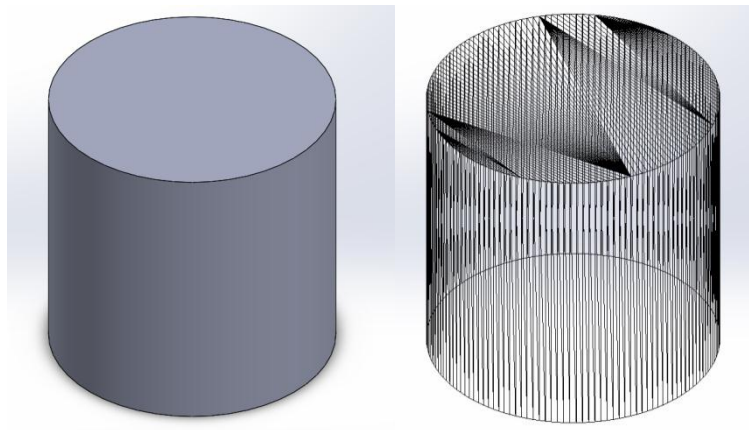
Cilindro modelado en CAD (Izquierda) y su conversión a STL (Derecha).
